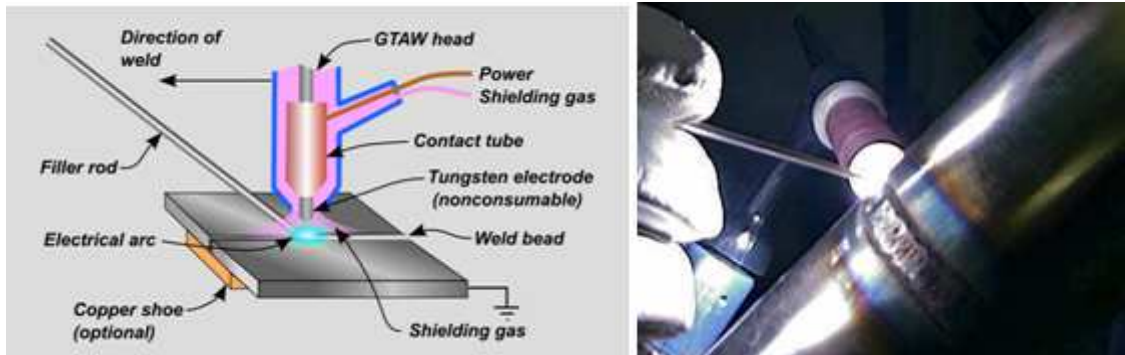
Soldadura WIG. Fuente: Ultrarad Technical Services.
